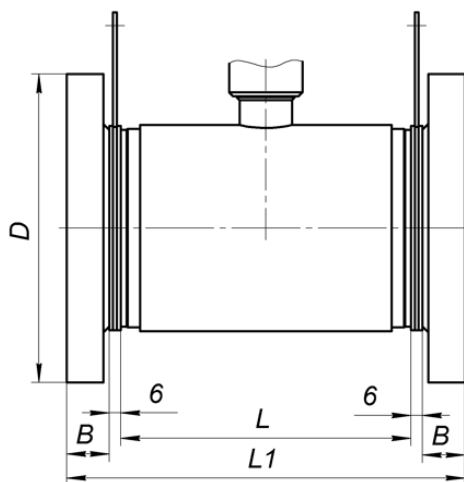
Габаритные размеры сборки расходомера вместе с ответными фланцами ГОСТ 33259-2015 (с кольцами заземления).
